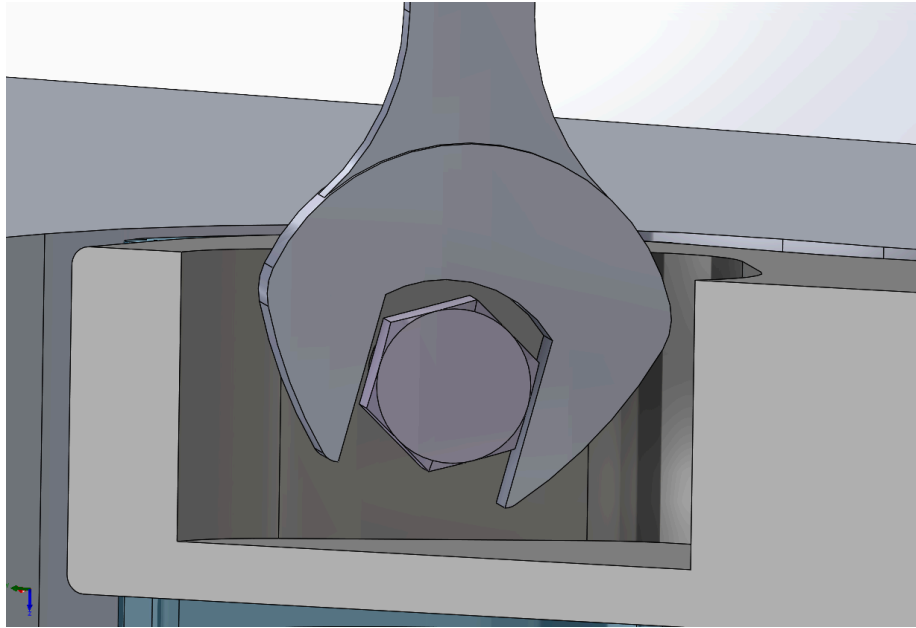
Una vista de sección que muestra que hay espacio para una llave inglesa de 9mm para apretar el tornillo.
